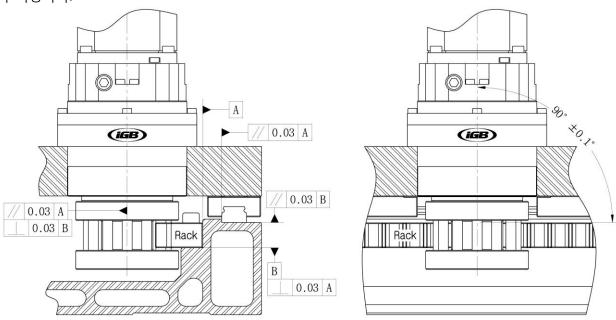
CRP 설치 예 [Figure 3. CRP installation examples]
